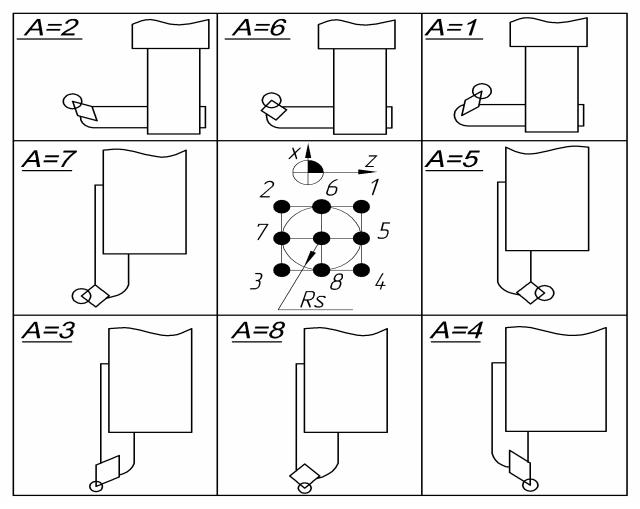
Кодирование рабочих вершин токарных инструментов
